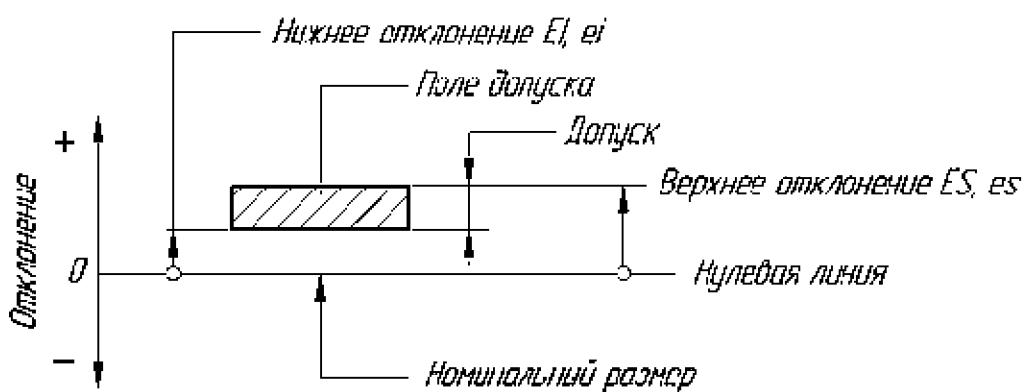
Расположение полей допусков вала и отверстия
